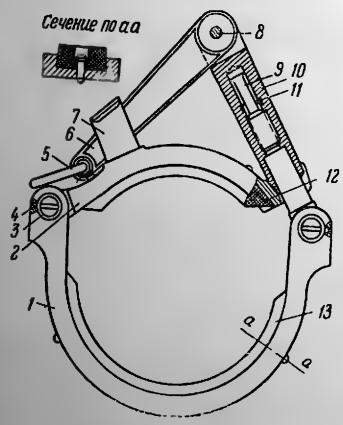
Обойма: 1 — нижняя обойма (1-44); 2 — верхняя кольцо (1-51); 9 — болт (1-52); 10 — зажимная гайка (1-50); 11 — штифт (1-53); 12 — верхний буфер (1-130); 13 — нижний буфер
